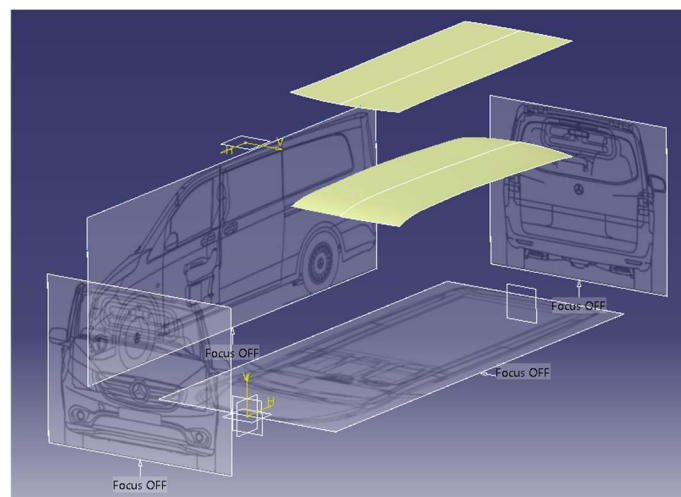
Digitalización del techo y proyección sobre un plano horizontal.
